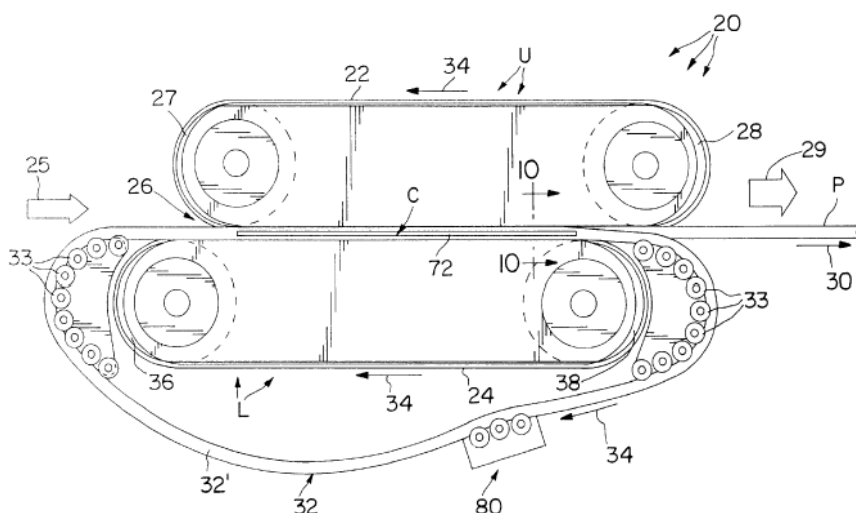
Схема усовершенствования системы управления дамб-блоками двухленточной литейной машины Хазелетт по патенту Германии № DE69927213 американской компании HAZELETT STRIP CASTING CORP (обозначения в тексте)
